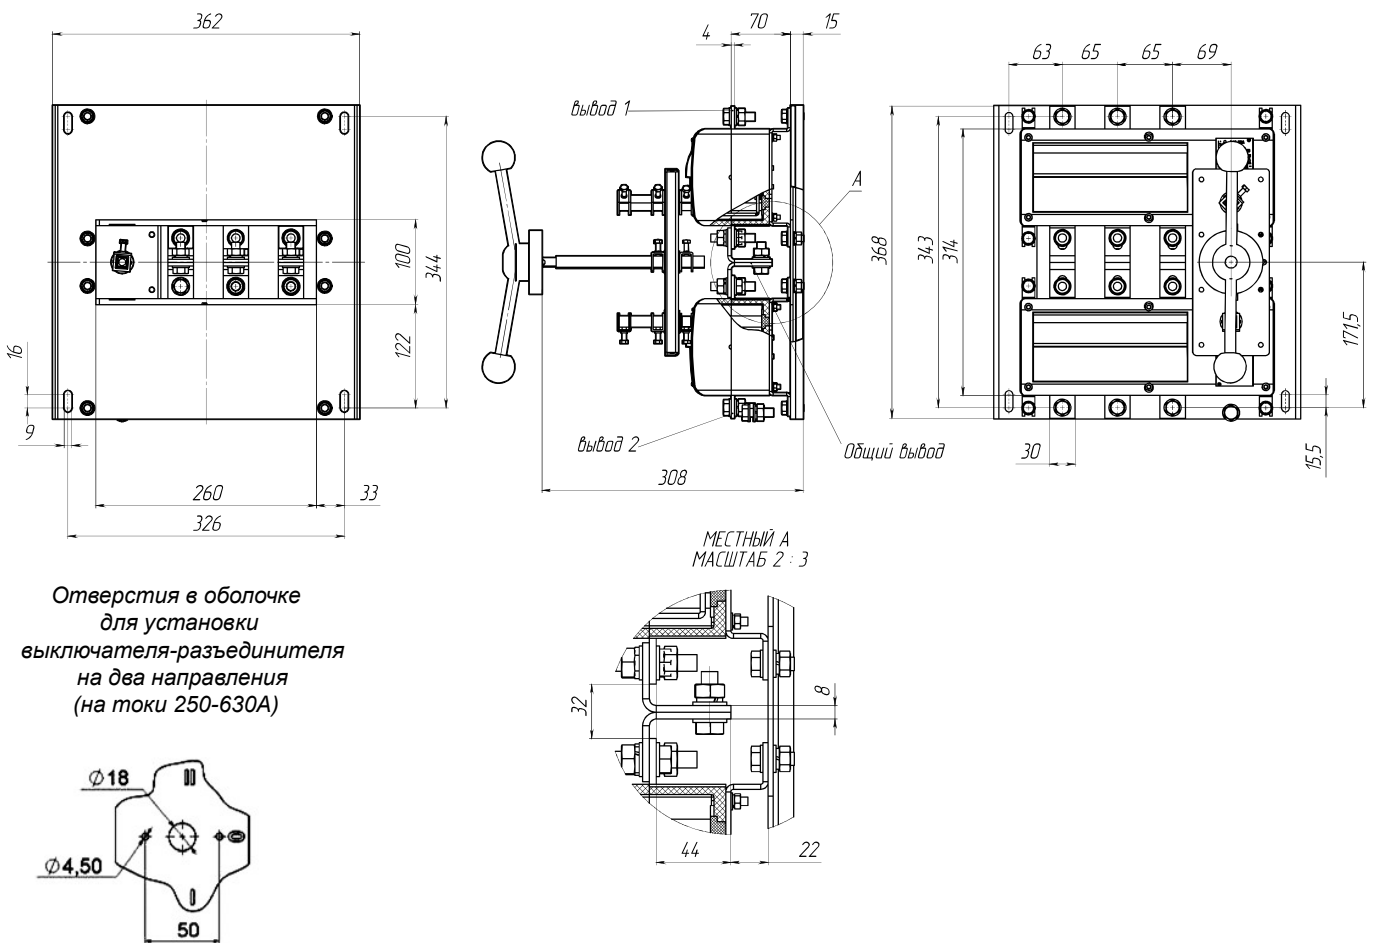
Выключатель-разъединитель ВНК-35-71130-32 УХЛ3 на два направления, масса не более 11,9 кг
